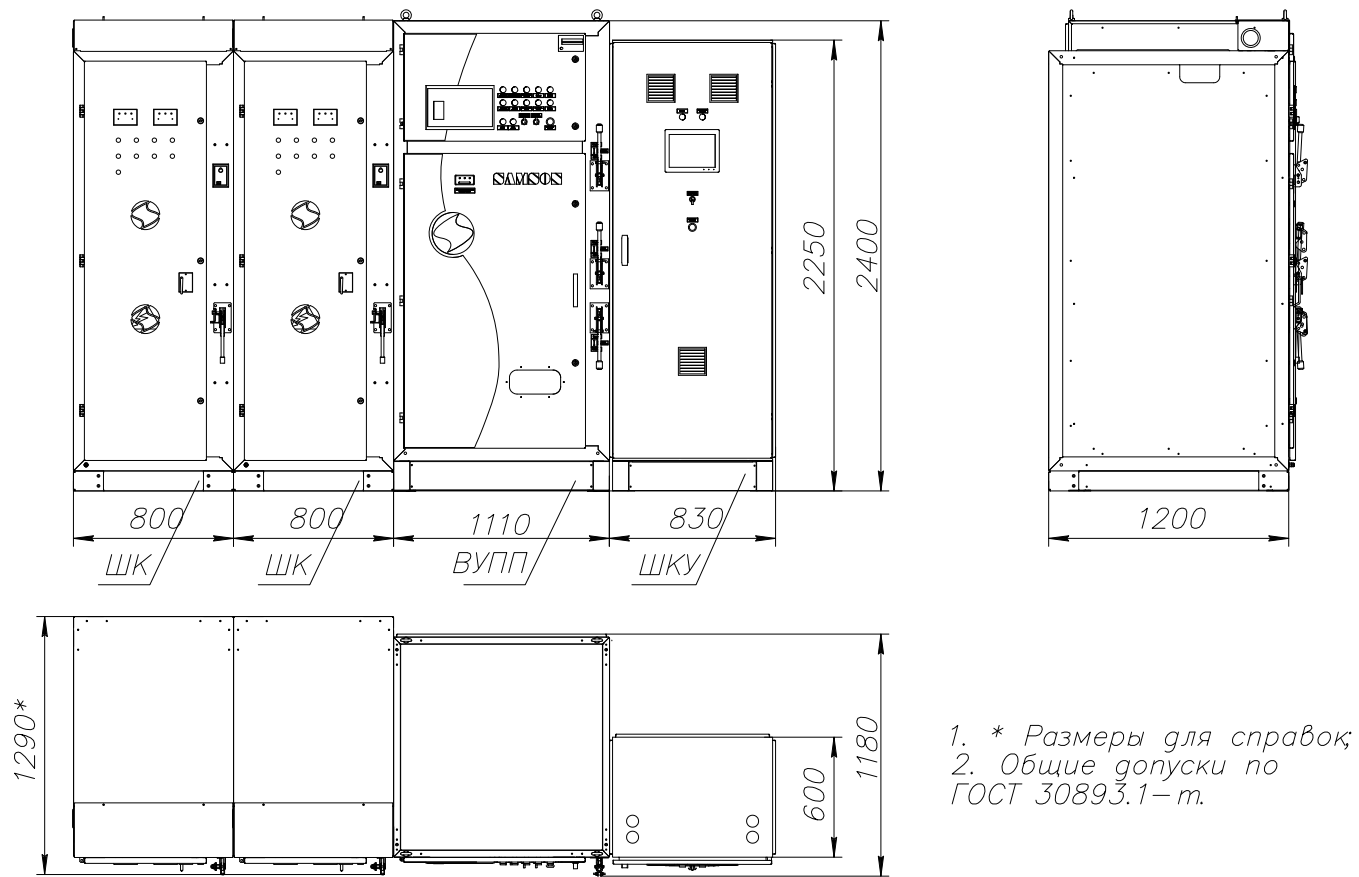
Габаритные размеры КВУПП «Самсон. Выборочный пуск двух двигателей.
